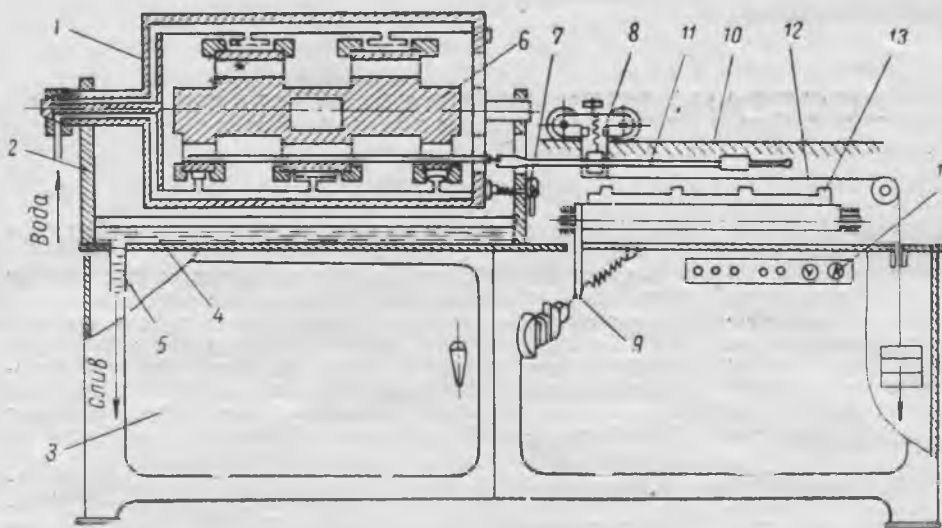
Схема установки для наплавки траков ТДТ-60:
